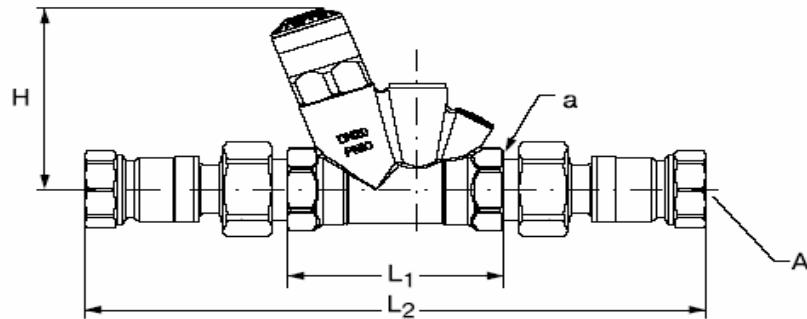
Габаритные и присоединительные размеры клапана МТСВ.
